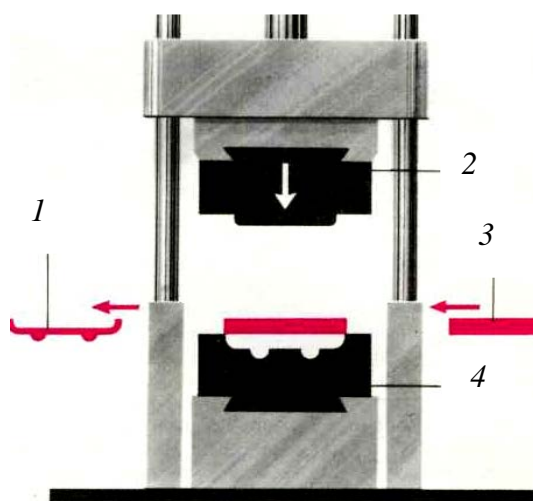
Штампування під пресом: 1 – готовий виріб; 2 – пуансон; 3 – заготовка; 4 – матриця.
